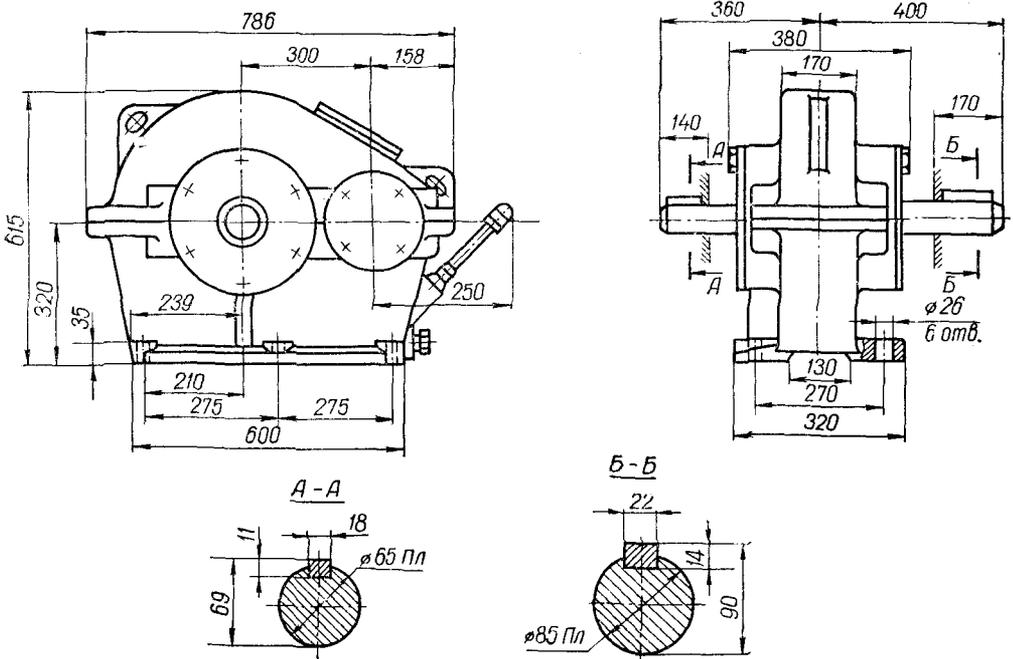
Основные и габаритные размеры редуктора ЦОМ-30.
